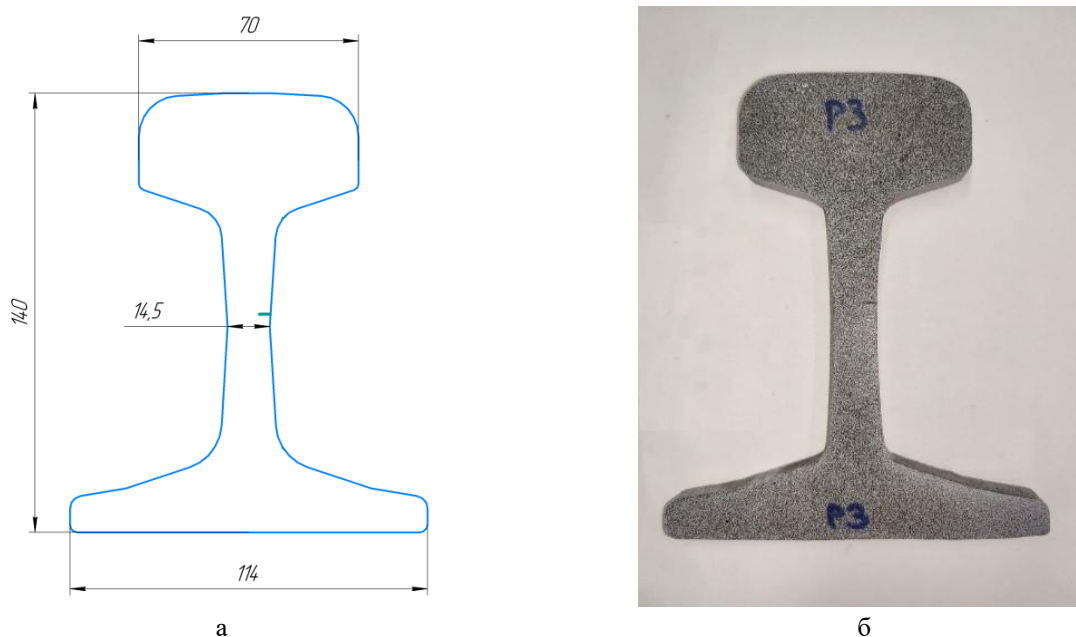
Чертеж (а) и внешний вид (б) рельса
